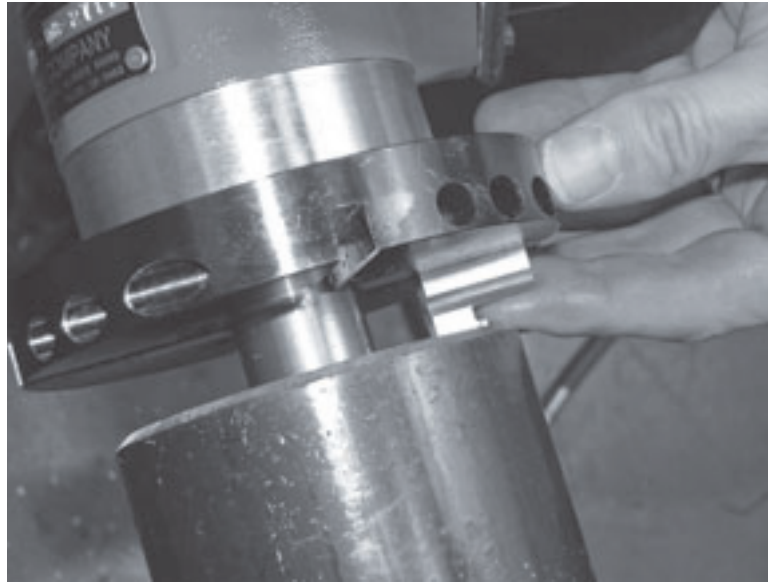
Führen Sie das Innenbearbeitungswerkzeugs ein, ziehen Sie jedoch nicht die Keilschrauben des Drehstahls an.
